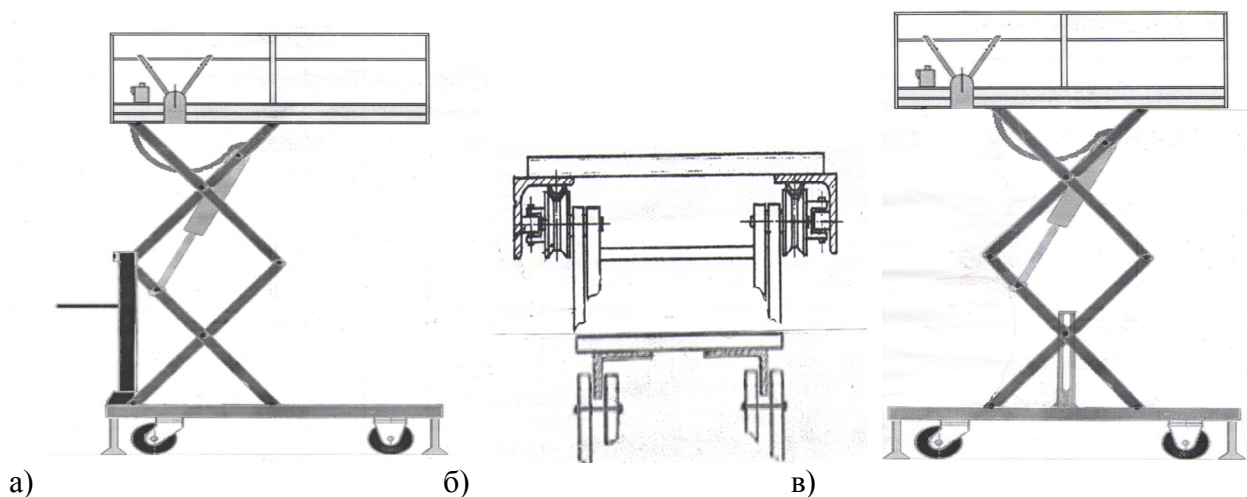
Схемы подмостей а) ПДМ-2.2, б) вид сверху на соединение конструкции с вертикальной стойкой в) смещение вертикальной стойки к среднему шарниру
